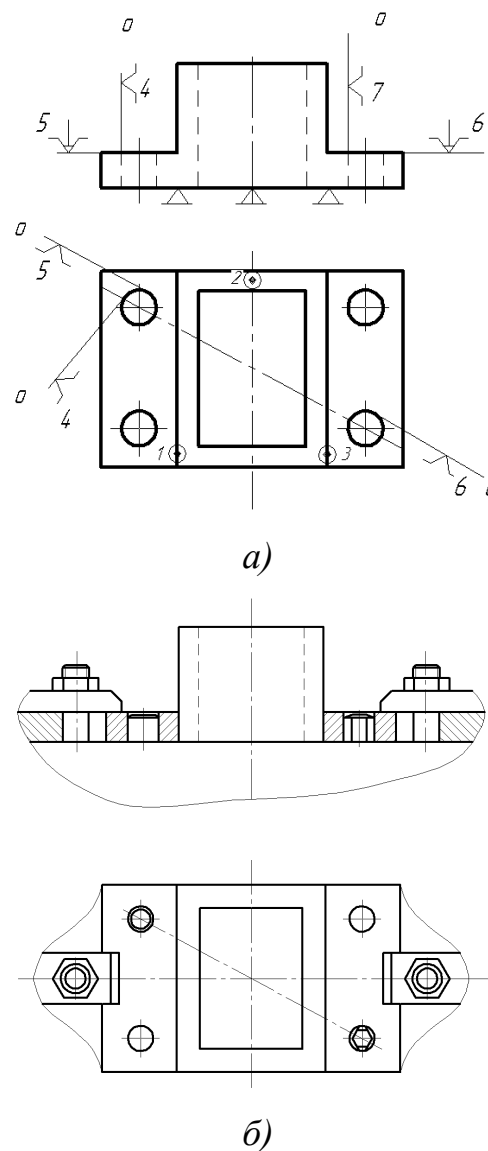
Схема базування корпусної деталі коробчастого типу по площині і двох отворах (а) та теоретична схема базування (б)
